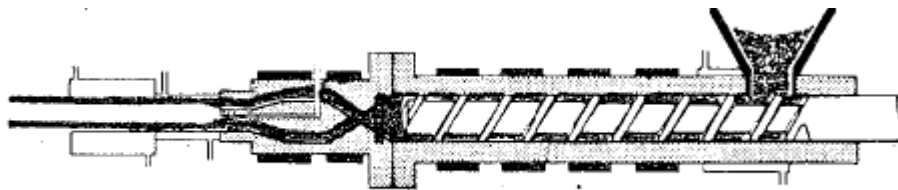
Partes principais de uma extrusora com exceção do motor e engrenagens.
